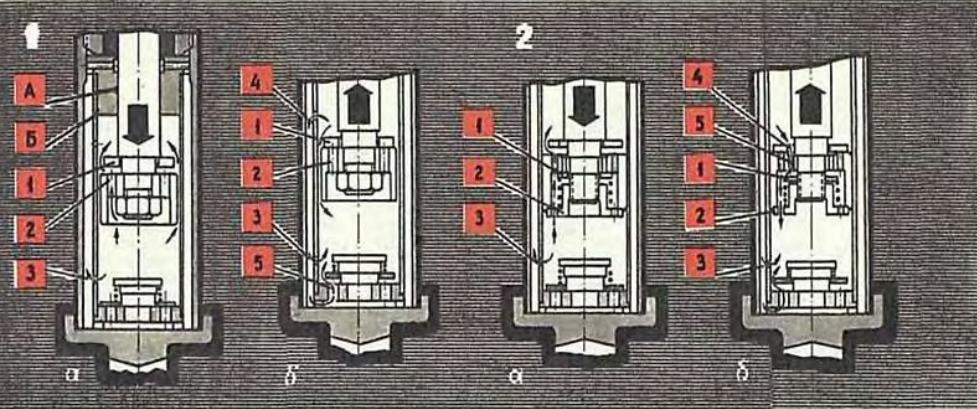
Амортизатор старой конструкции: а — ход сжатия; б — ход разжатия; А — зазор между штоком и направляющей втулкой; Б — зазор между цилиндром и направляющей втулкой.
